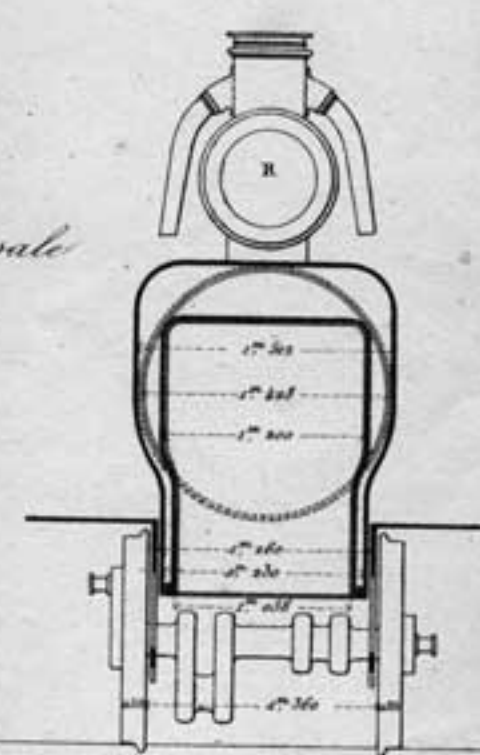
Coupe transversale par le foyer. Transverse section through the firebox showing the internal structure and dimensions.
